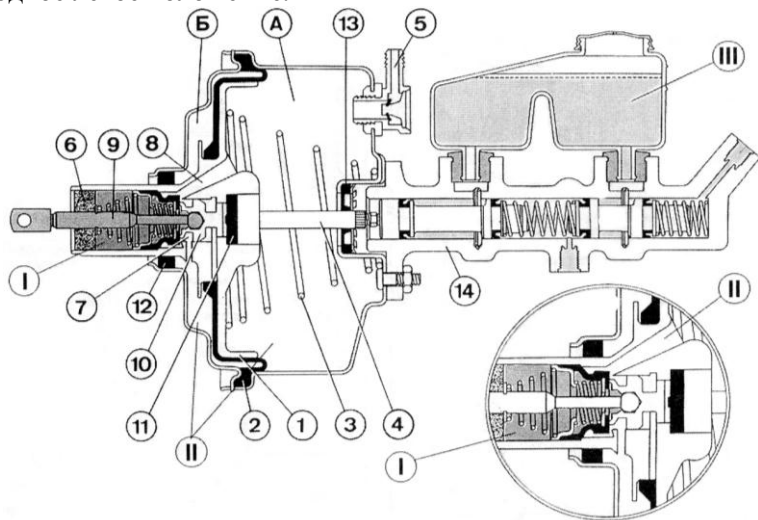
Детали вакуумного усилителя типа «mastervac» в исходном положении: I – атмосферное давление; II – давление разрежения; III – жидкость; IV – жидкость под давлением; 1 – поршень; 2 – диафрагма; 3 – возвратная пружина; 4 – шток поршня; 5 – обратный клапан; 6 – воздушный фильтр; 7 – канал атмосферного клапана; 8 – канал вакуумного клапана; 9 – толкатель; 10 – плунжер; 11 – буфер
